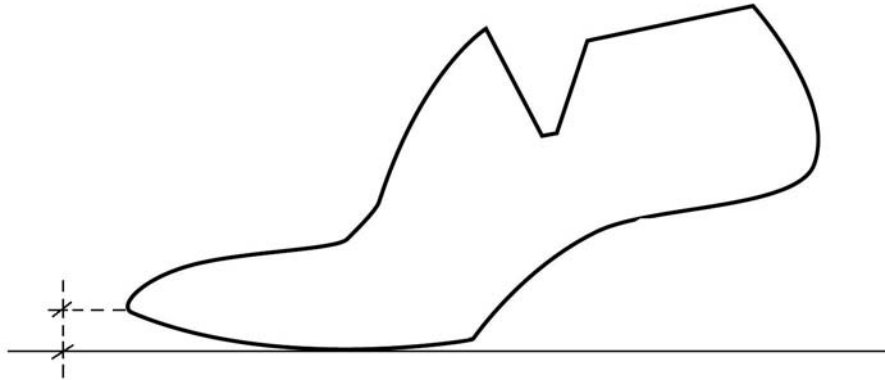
Distance verticale entre le plan de base et le bout de la forme correctement placé en ce qui concerne la hauteur du talon.
